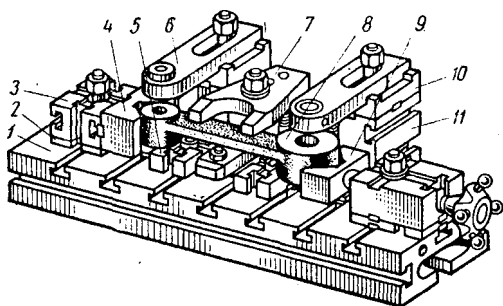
Универсально-сборное приспособление для обработки отверстий в рычагах
